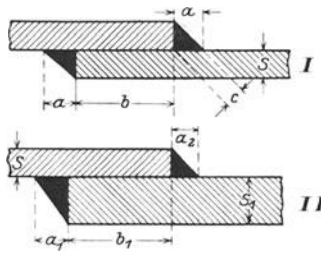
Abmessungen bei überlappten Schweißungen.
